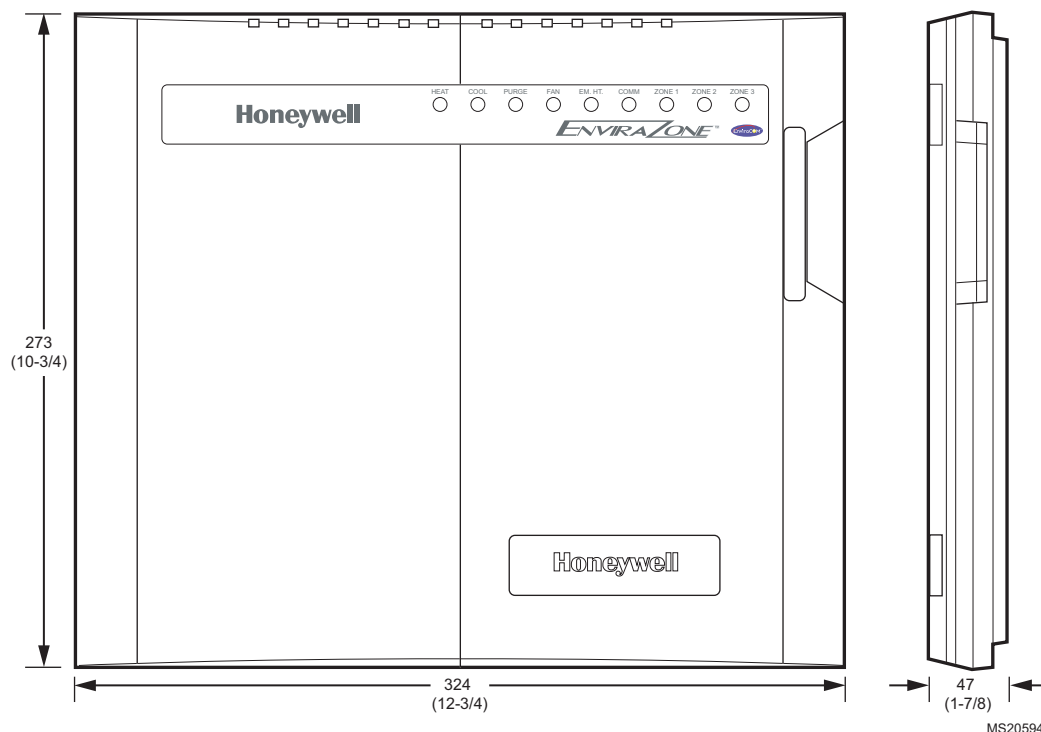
Dimensiones del W8835 en pulgadas (mm).
